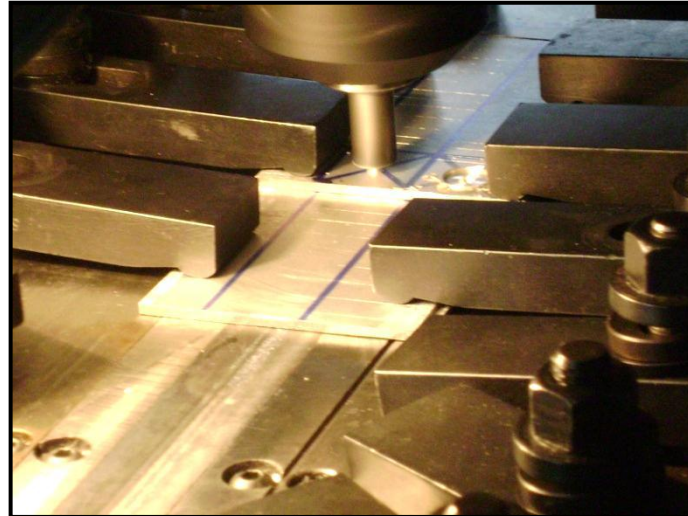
Procedimiento de soldadura por fricción-agitación de punto en la máquina especializada [78]
